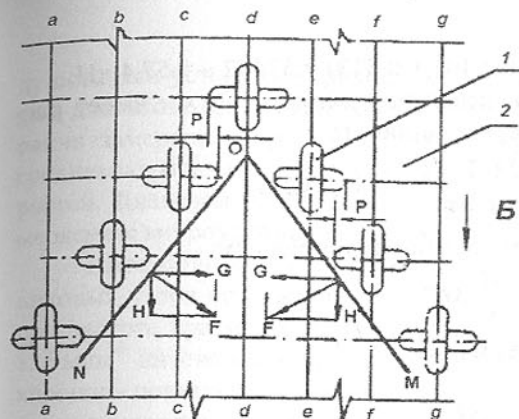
Схема расположения отрезков цепей на поверхности ротора (развертка)
